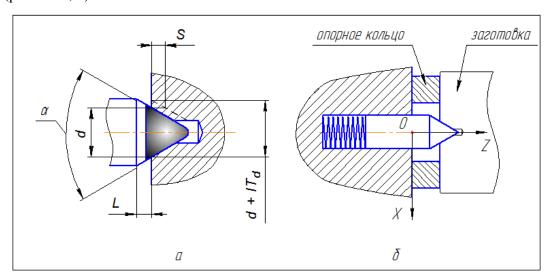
Установка в центрах: а – жесткий центр; б – плавающий центр с опорным кольцом
